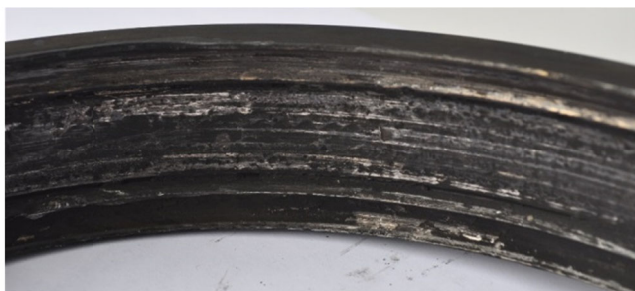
Внешний вид рабочей поверхности наружного кольца
